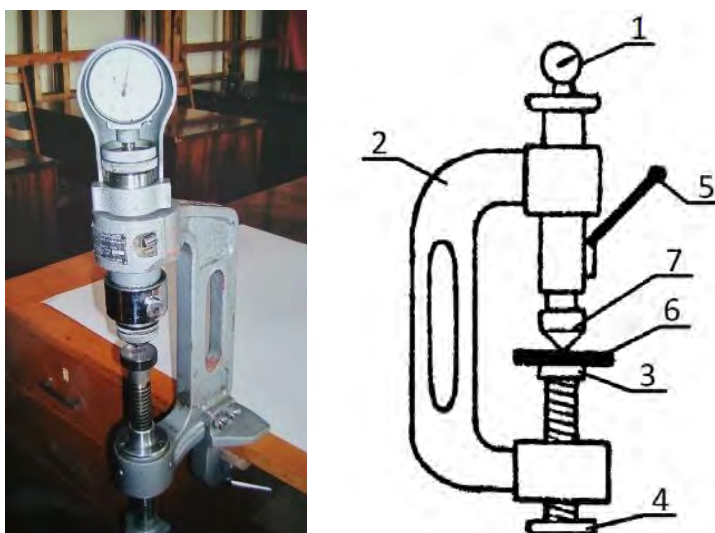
Общий вид и схема устройства прибора Рокуэлла: 1 – индикатор; 2 – рама прибора; 3 – столик; 4 – маховичёк; 5 – ручка приложения нагрузки; 6 – испытываемый образец металла; 7 – вдавливаемая насадка (конус или шарик)
